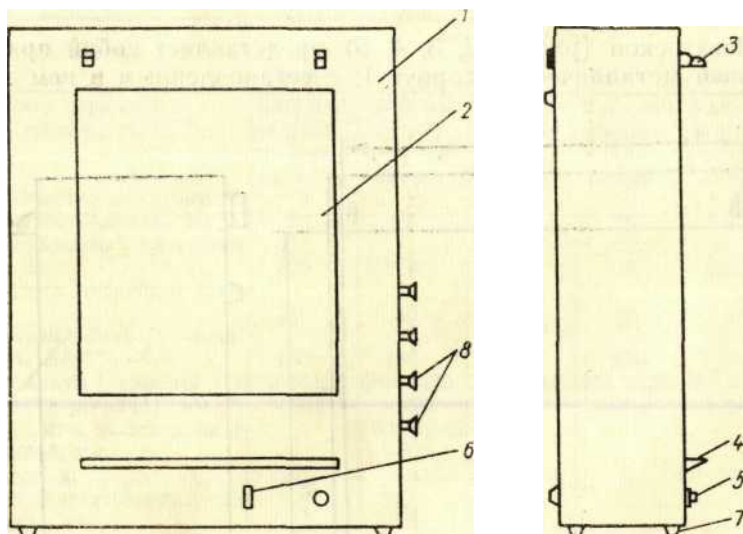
Негатоскоп общего назначения с диафрагмирующими шторками НШ-48. Общий вид
